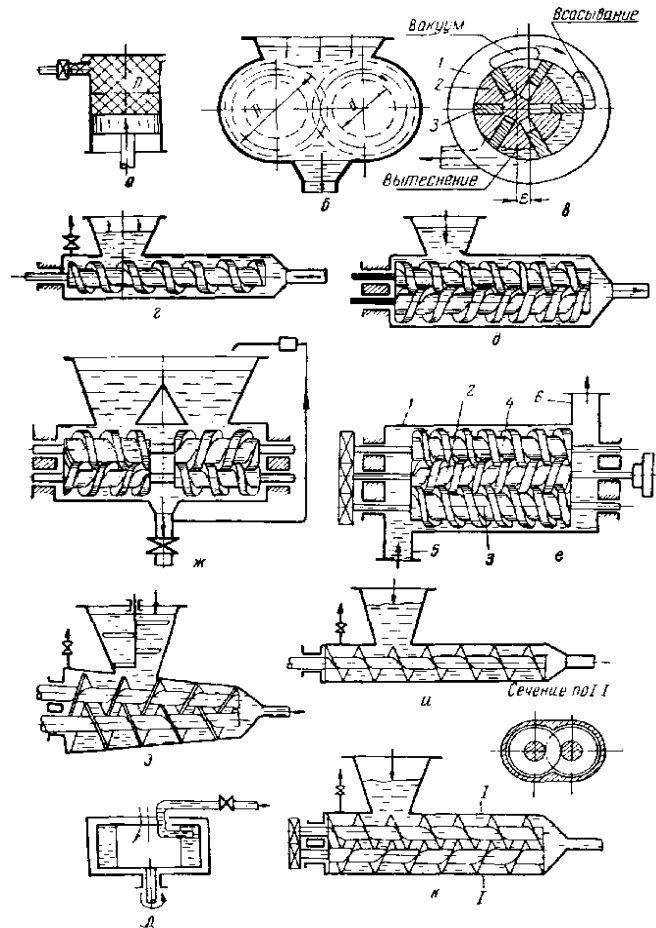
Кинематические схемы вытеснителей шприцов [96]: а - поршневые; б - шестеренные; в - пластинчатые; г - ж- с цилиндрическим винтом; з - с коническим винтом; и – одношнековый; к - двухшнековый, л – центробежный
